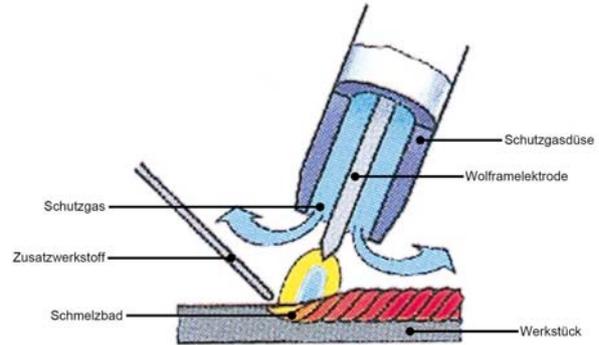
Funktionsprinzip WIG-Schweißen
